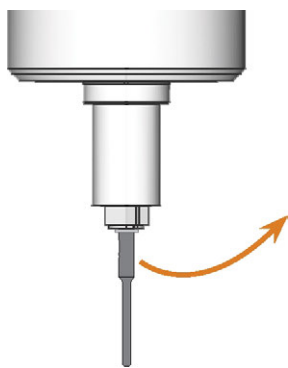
RIMOZIONE DELL'UTENSILE DALLA PINZA DI SERRAGGIO
